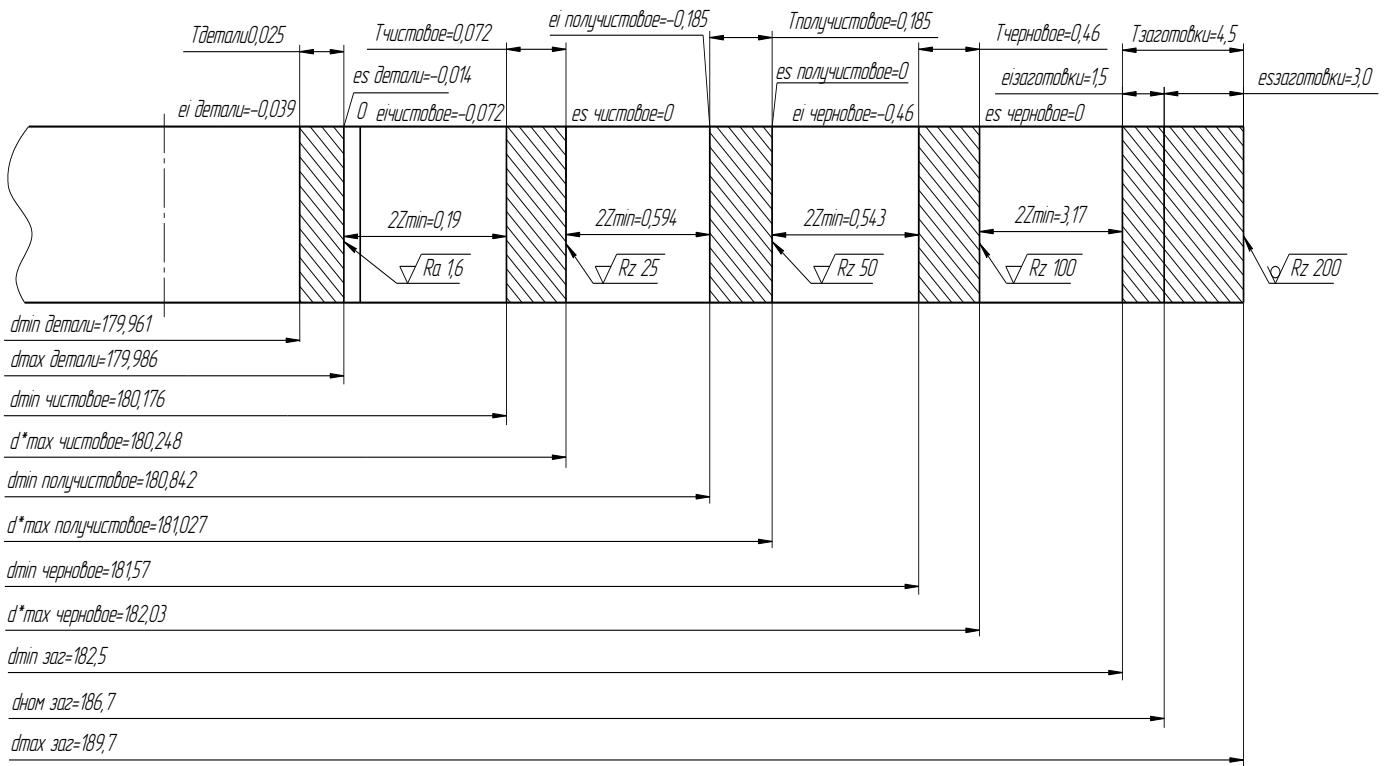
Схема расположения припусков и допусков для наружной цилиндрической поверхности  $\varnothing 180g6(-0,014;-0,039)$
